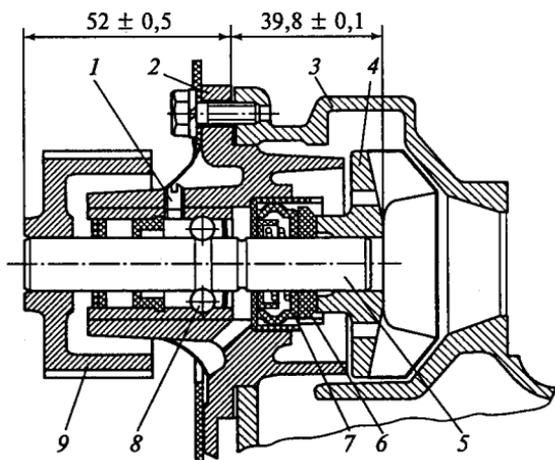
Насос охлаждающей жидкости с контрольными размерами для сборки:
